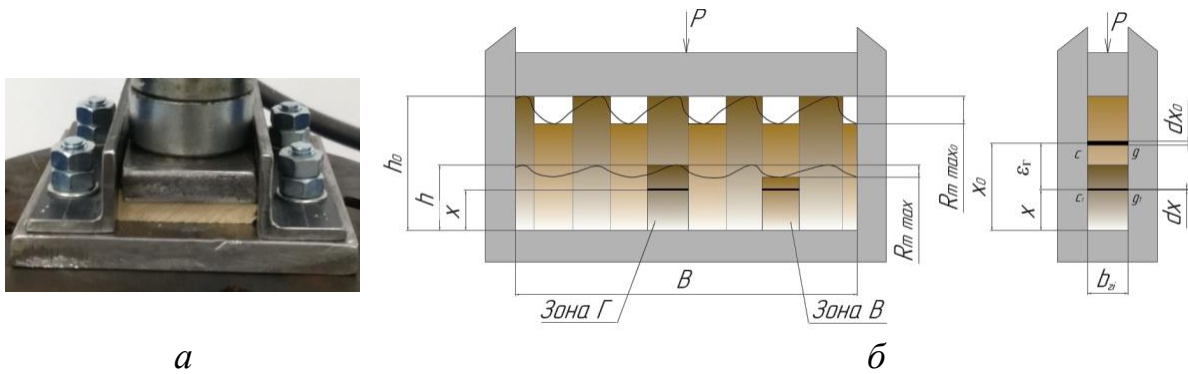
Прессование заготовки, подвергнутой обжигу и брашированию:
